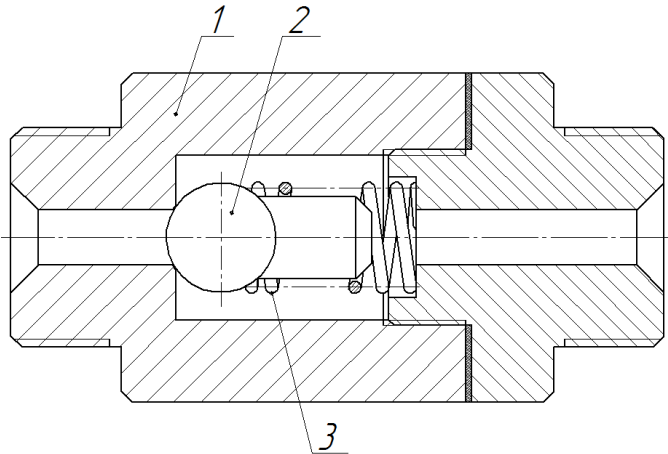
Перепускной клапан: 1- корпус; 2- двойной запорный элемент; 3- пружина клапана
